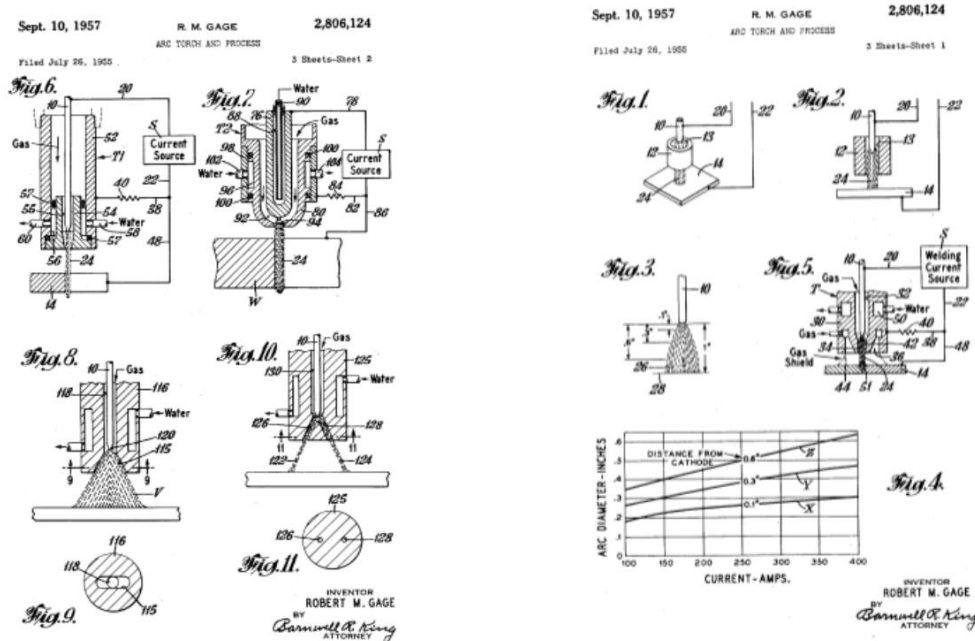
Patente de Robert M. Gage en 1957: soldadura por arco de plasma (PAW) (107)
